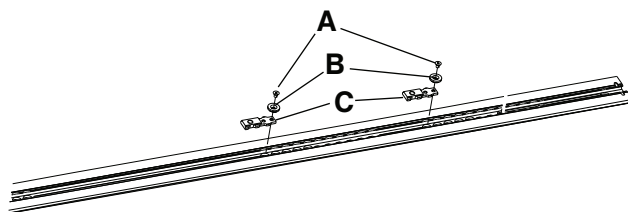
Inserire la staffa di fissaggio per la piastra a pavimento
